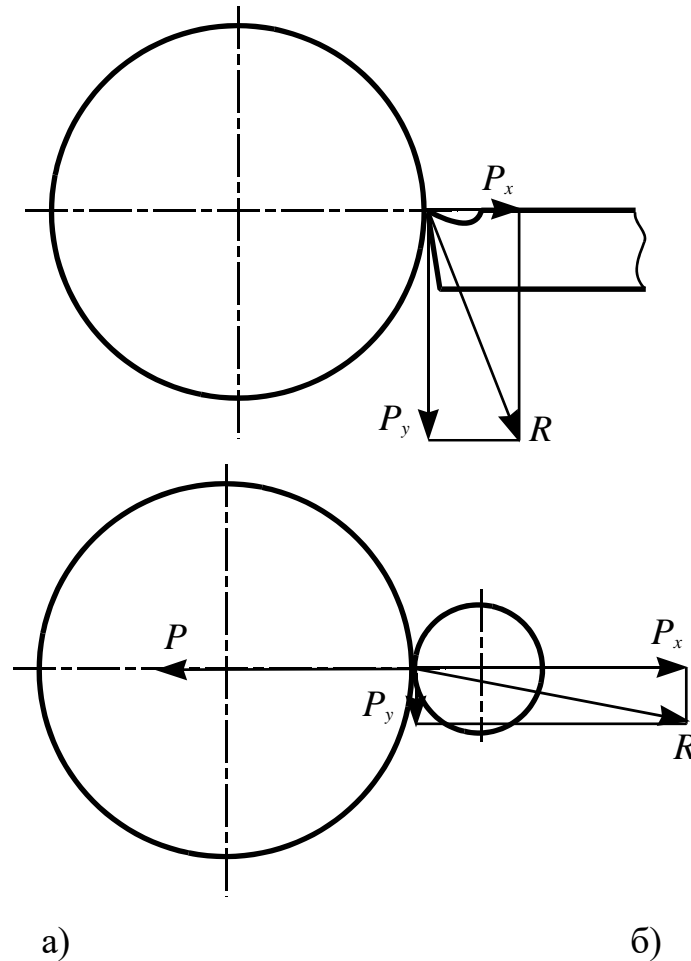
Схема сил, які діють на деталь і інструмент в процесі обробки різанням (а) і пластичним деформуванням (б) на токарному верстаті
